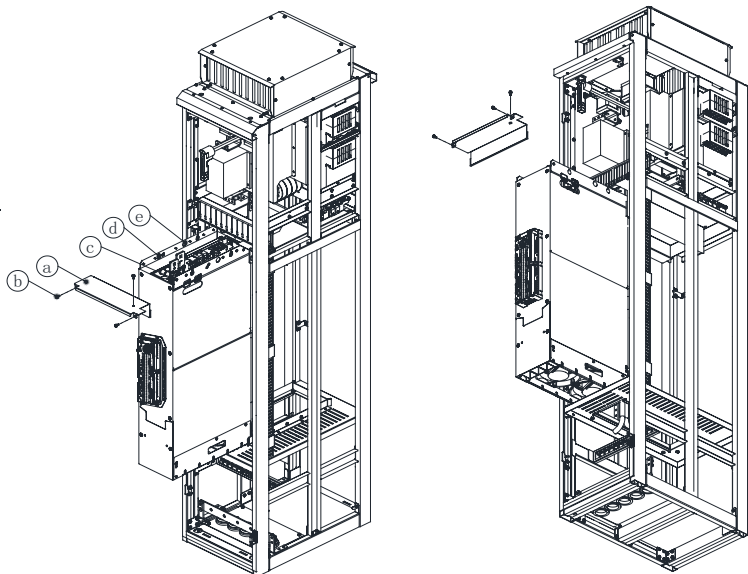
Замена вентилятора инверторного блока типоразмеров Н6...Н7
